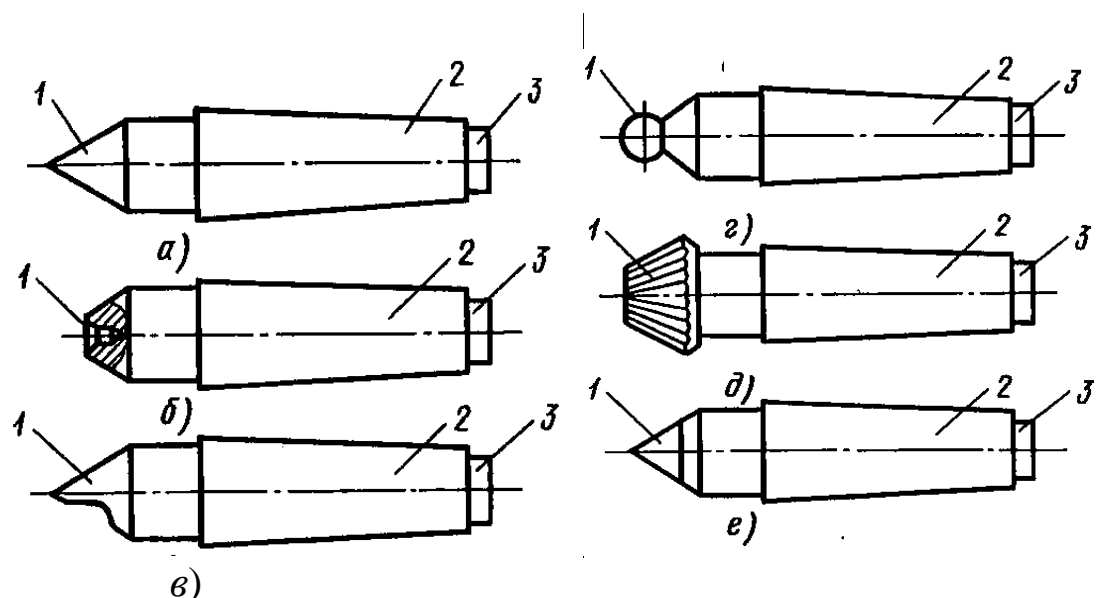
Типы центров: а – упорный; б – обратный; в – срезанный; г – со сферической рабочей поверхностью; д – с рифлёной рабочей поверхностью; е – с твердосплавной рабочей частью
